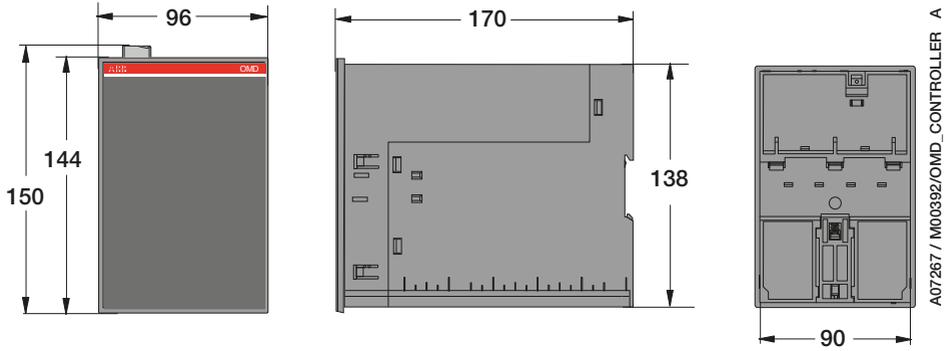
OMD200 und OMD300, Abmessungen des Geräts
